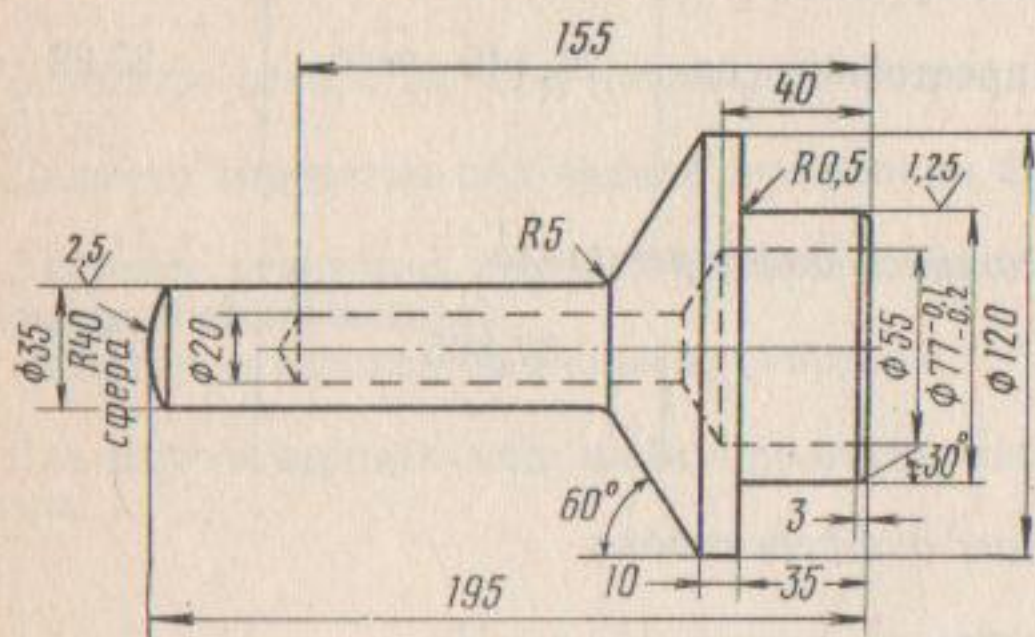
Оправка для запрессовки подшипников промежуточного вала
